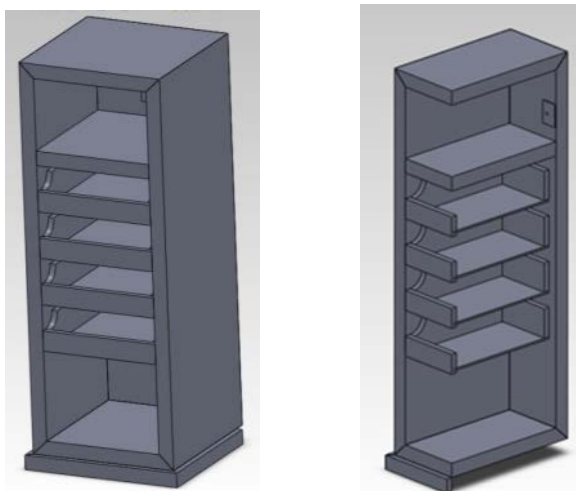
Bloco de arrumação em madeira. Vista de secção [1].
